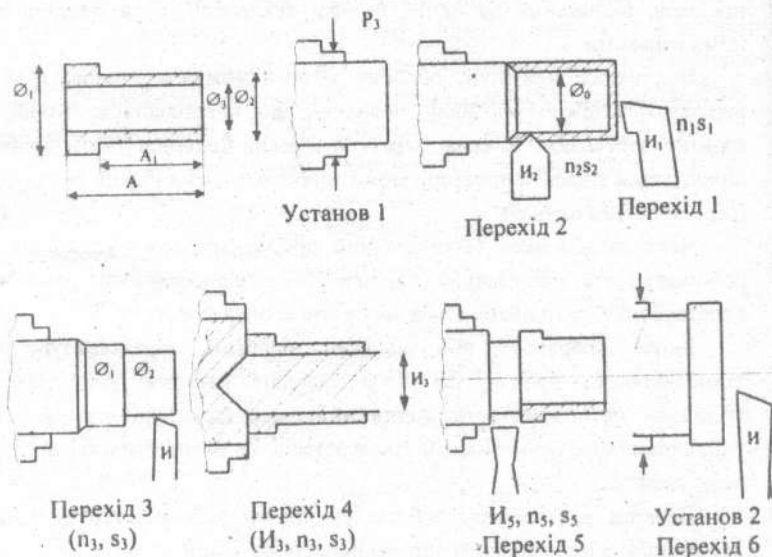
Послідовність виготовлення деталі-втулки на токарному верстаті
